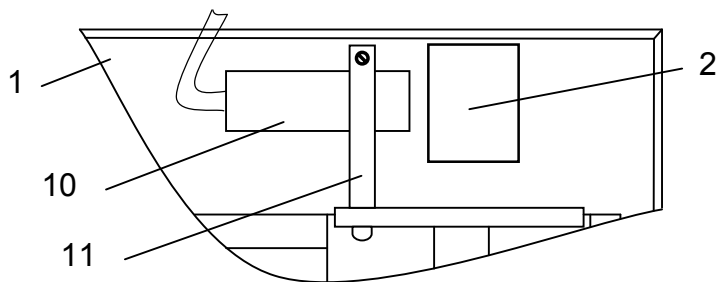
б. Установка датчиков ВК-316ОС, ВК-316ОС.02 на приспособление СП-20.
